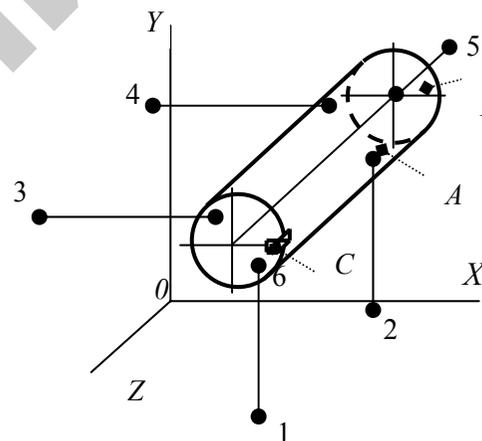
Базирующие поверхности и опорные точки цилиндрического изделия
